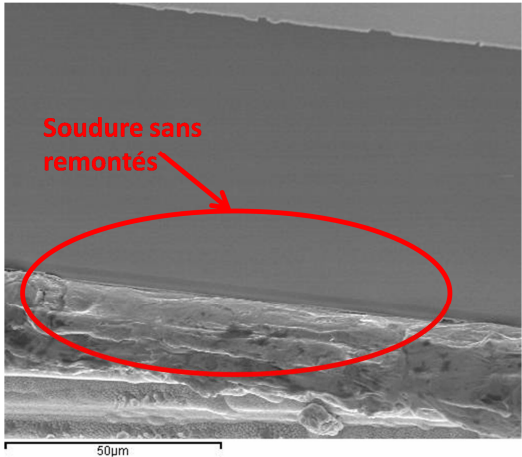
Photo MEB de la facette de sortie d'un laser large sans remontée de soudure
